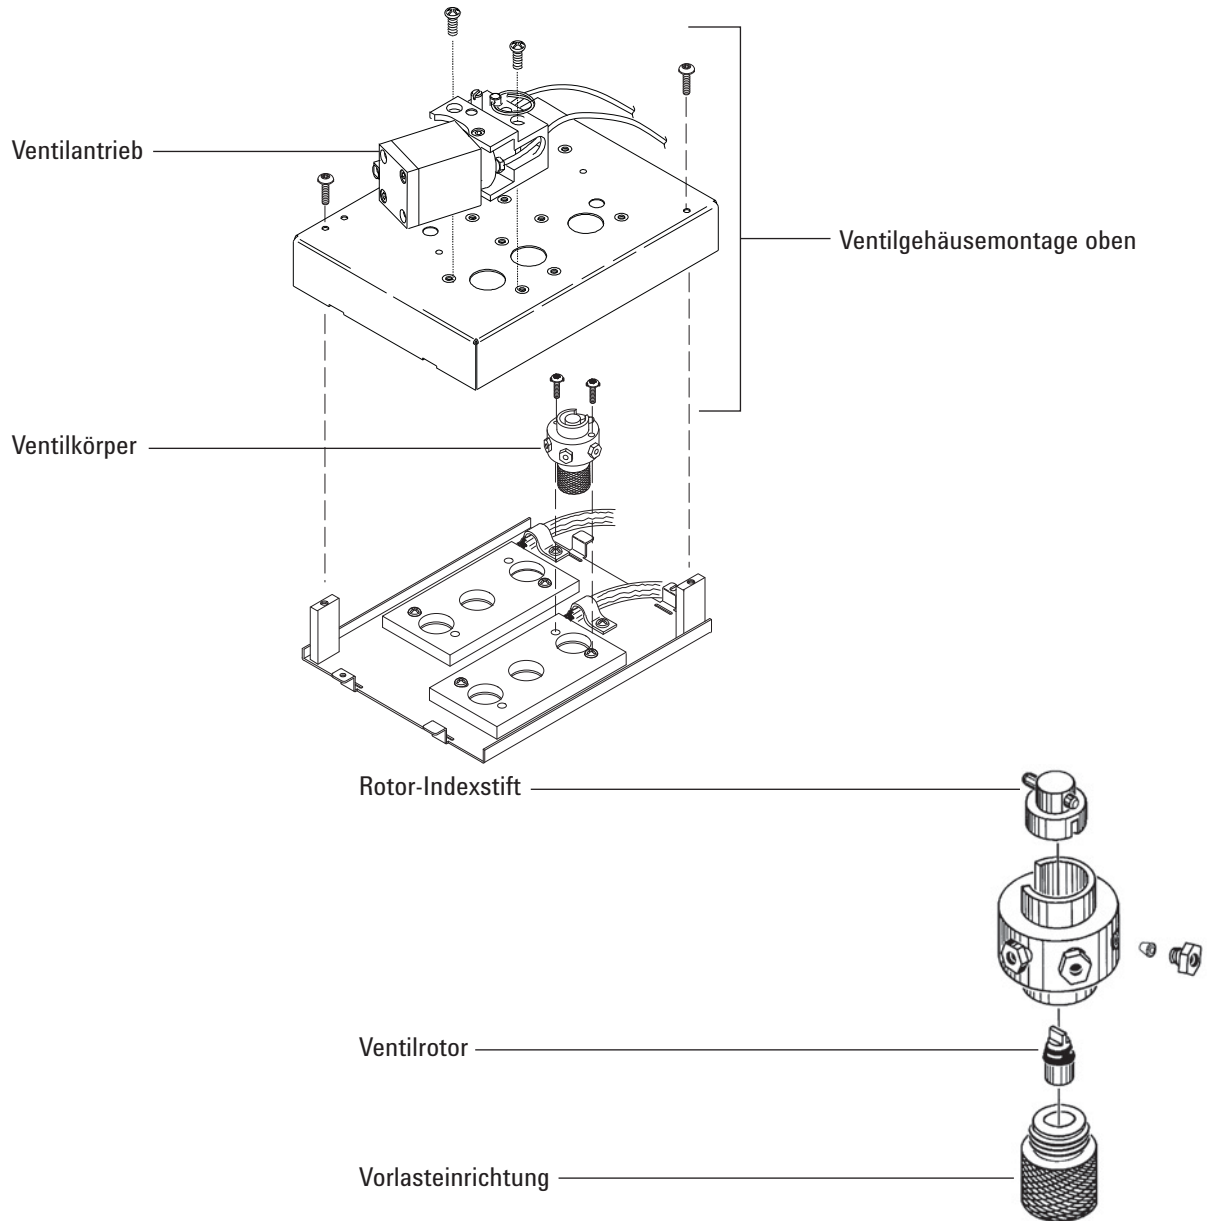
Explosionsansicht von Teilen für das GC-Drehventil
